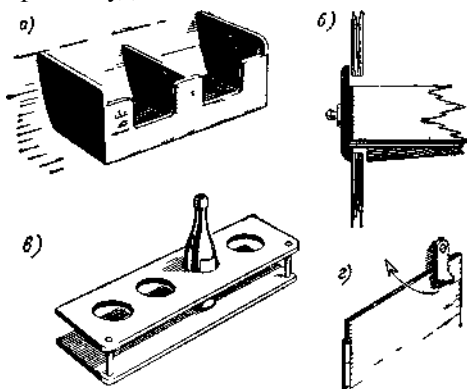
Детали оборудования каюты: а — полка для посуды; б — стопор для выдвижного ящика; в — полочка для бутылок и стаканов; г — стопор для дверцы шкафа.
